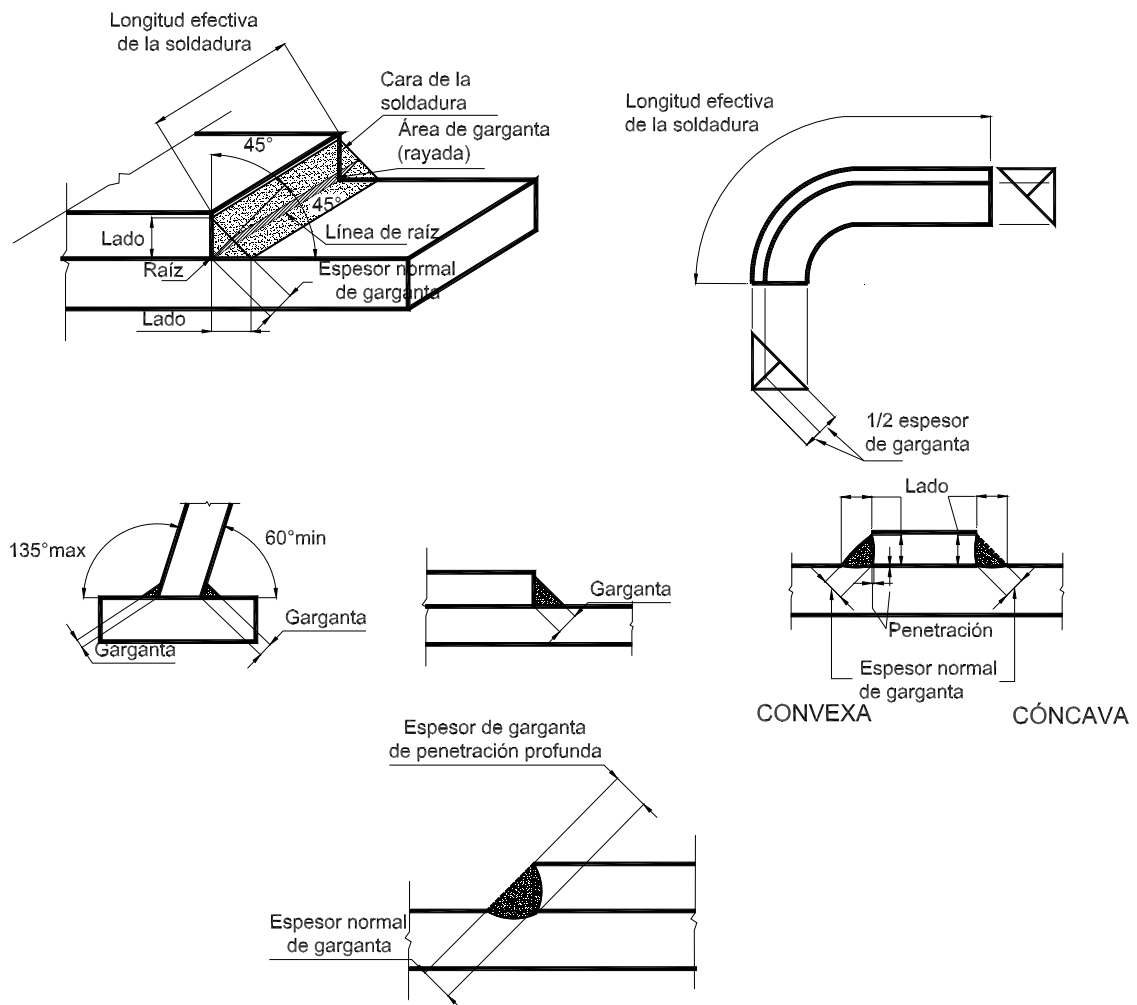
Nomenclatura de soldaduras de filete.
